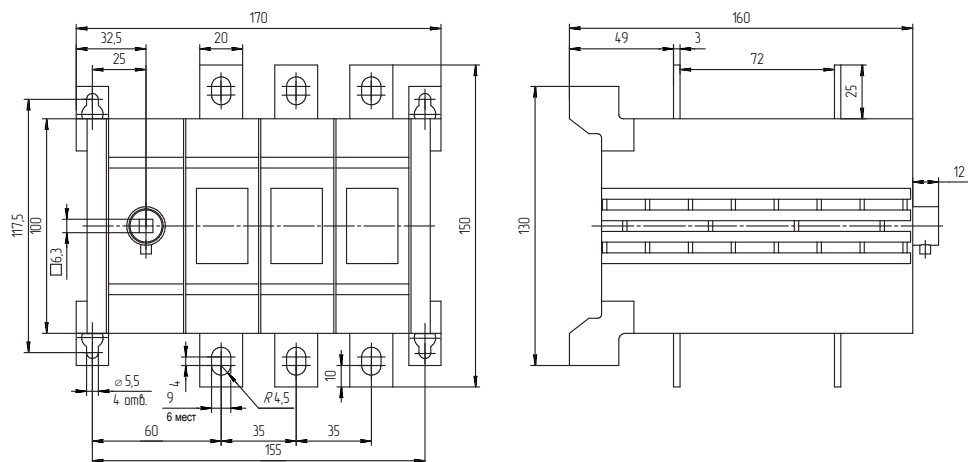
Выключатель-разъединитель 160 – 250 А реверсивного исполнения
